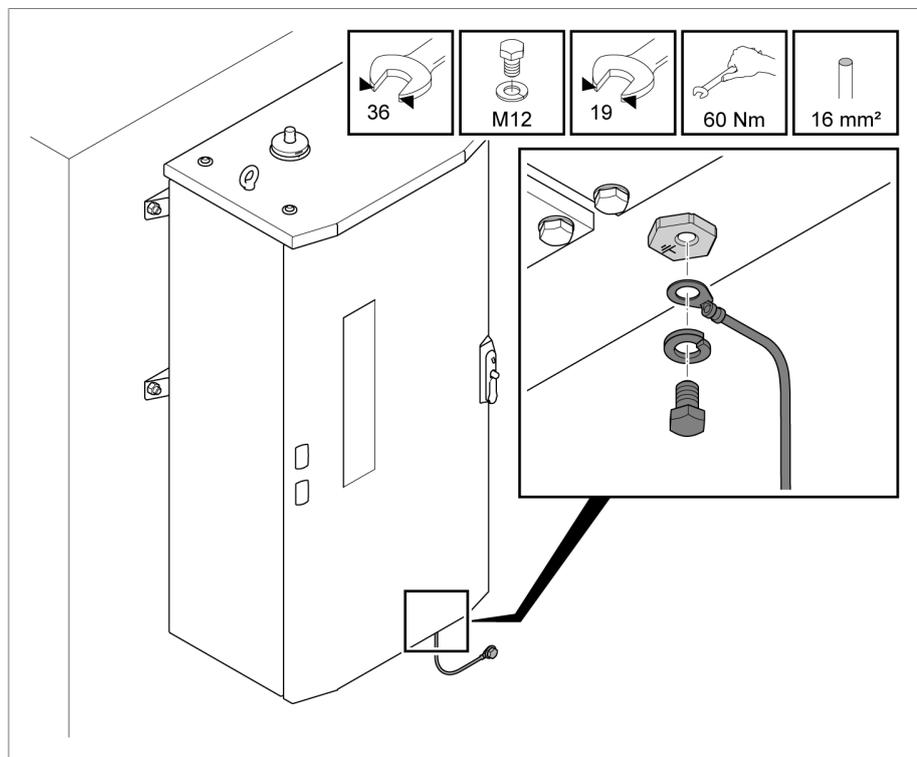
Erdungskabel am Steuerschrank anschließen
